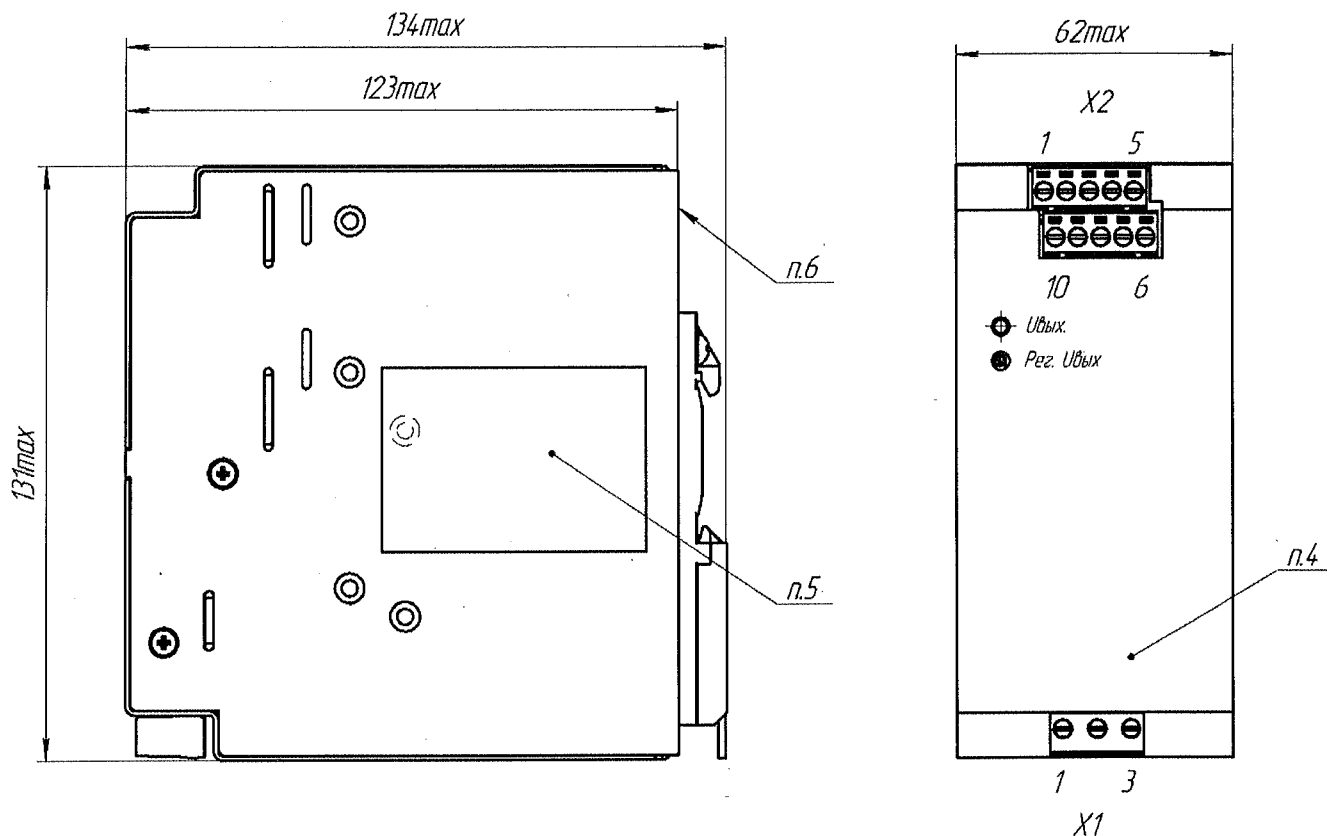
Габаритные размеры модуля КАН-Д240
